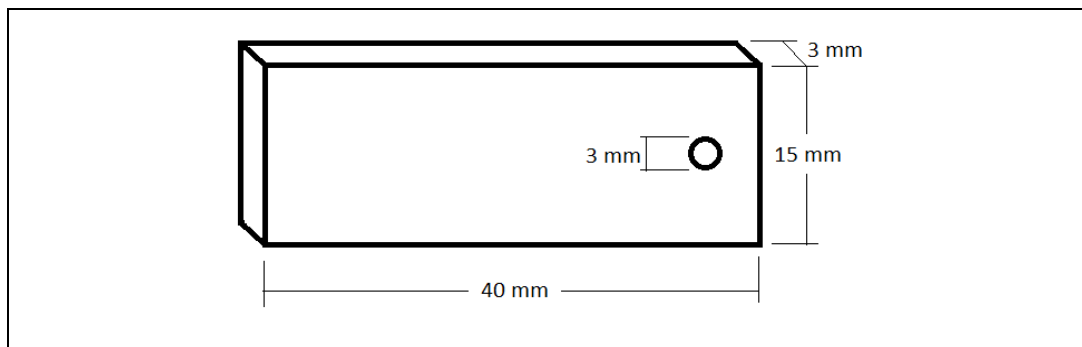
Imagem das dimensões dos corpos de prova de aço AISI 1020.
